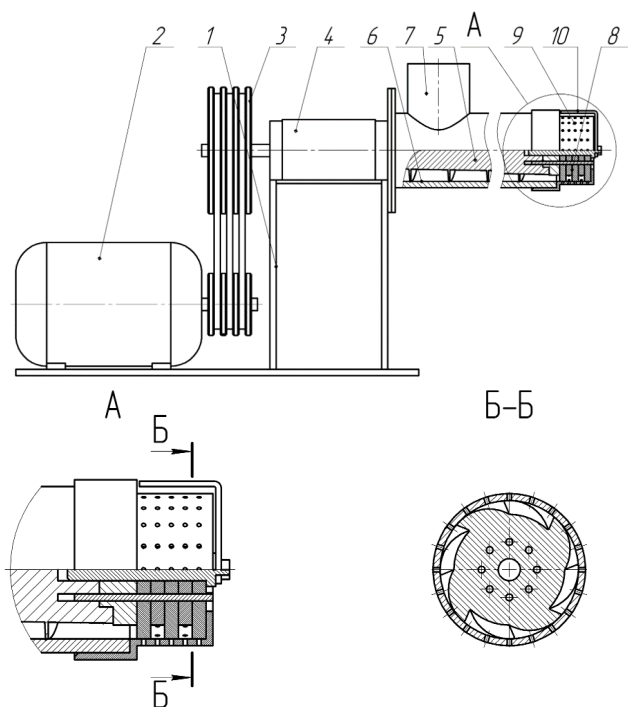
Конструктивно-технологічна схема установки для виготовлення пелет (пелетератора): 1 – рама; 2 – електродвигун; 3 – шків; 4 – підшипниковий вузол; 5 – гвинт; 6 – циліндричний корпус; 7 – завантажувальний бункер; 8 – формуючий кулачок; 9 – циліндрична матриця; 10 – ніж
